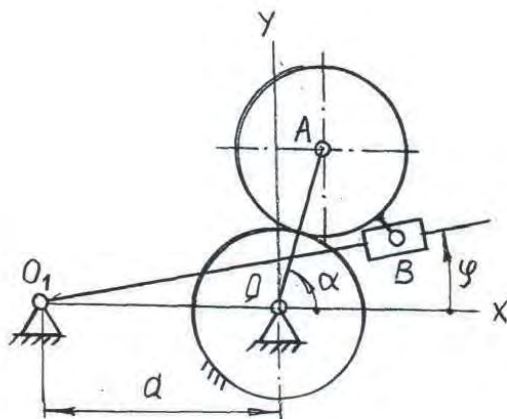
Зубчато-рычажный механизм с внешним зацеплением колес
